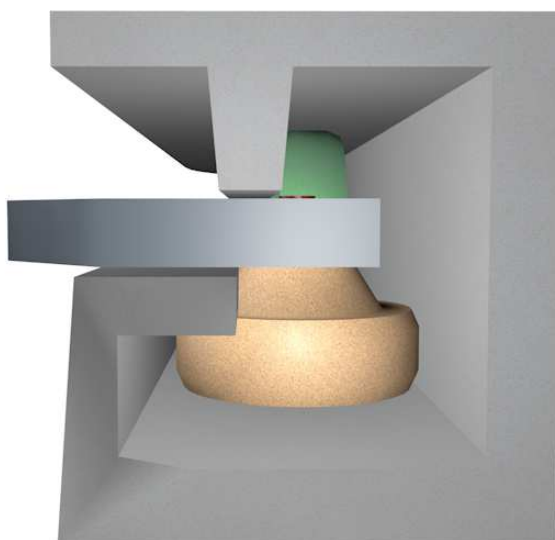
Inovace mechanismu (Zdroj: Autor)
